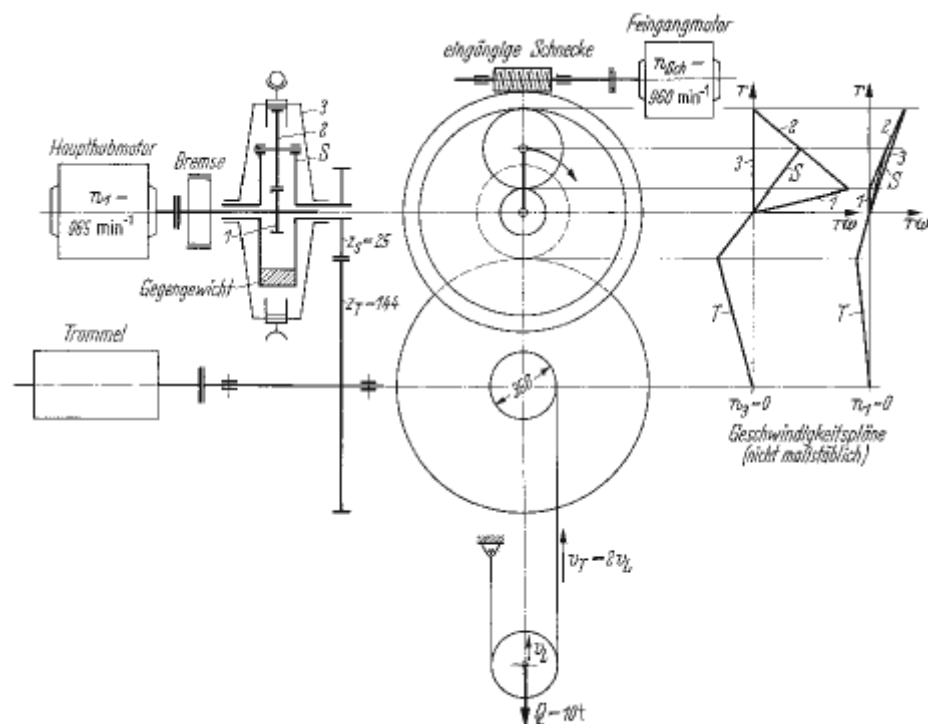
Umlaufgetriebe für Kranhubwerk (Beispiel 1)
